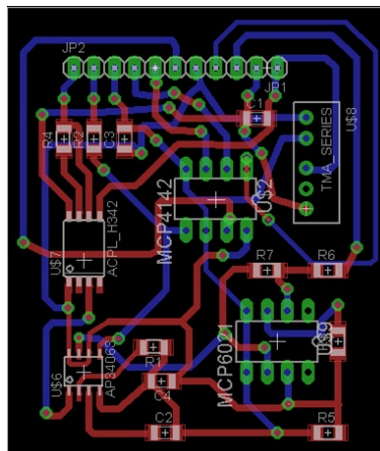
Desenho da PCB da placa de controlo do *buck
